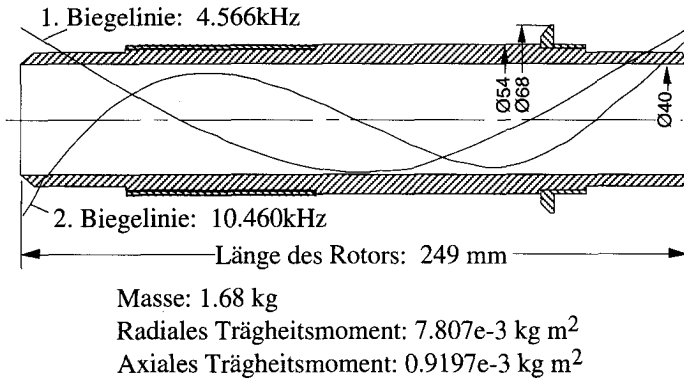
Rotor mit eingezeichneter 1. und 2. Biegelinie (frei schwebender Rotor)
